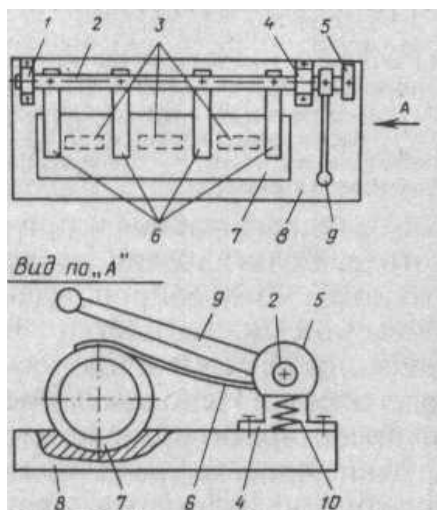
Гнездообразная опора с прижимным устройством: 1,4 - стойки; 2 - ось; 3-зоны сварки; 5 - кулачок; 6 - плоские пружины; 7 - изделие; 8 - основание; 9 - рукоятка; 10 - пружина фиксатора
